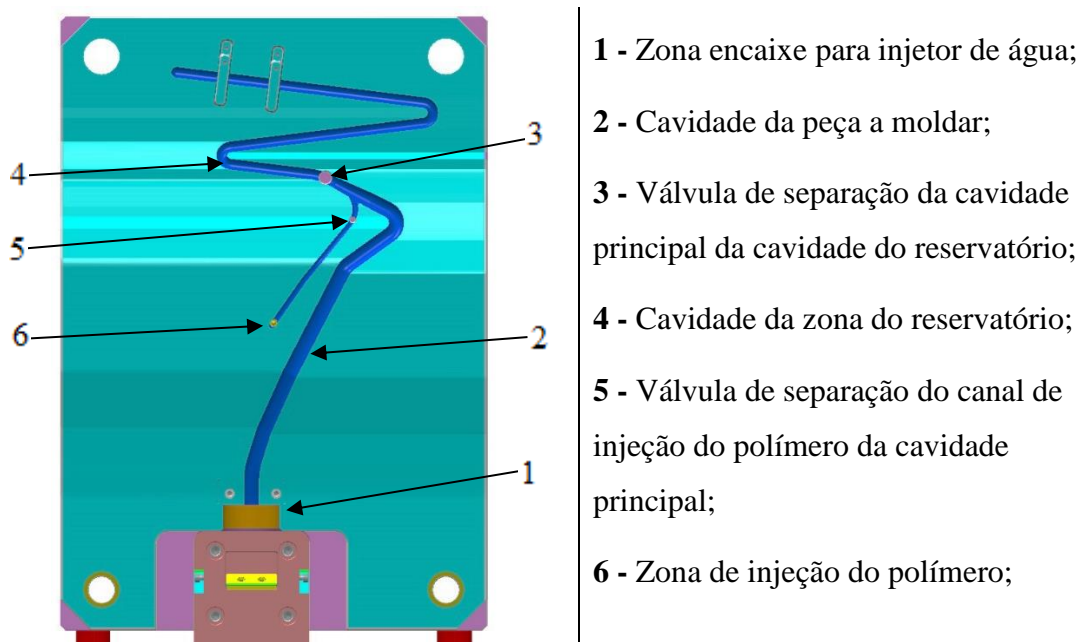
Chapa zona moldante do molde protótipo industrial 1
